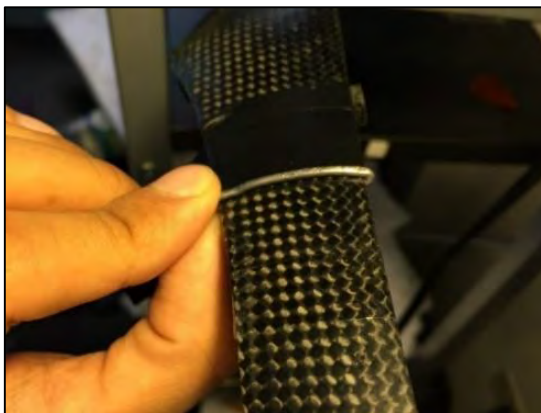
Envolver el perfil mediante un alambre de soldadura.
